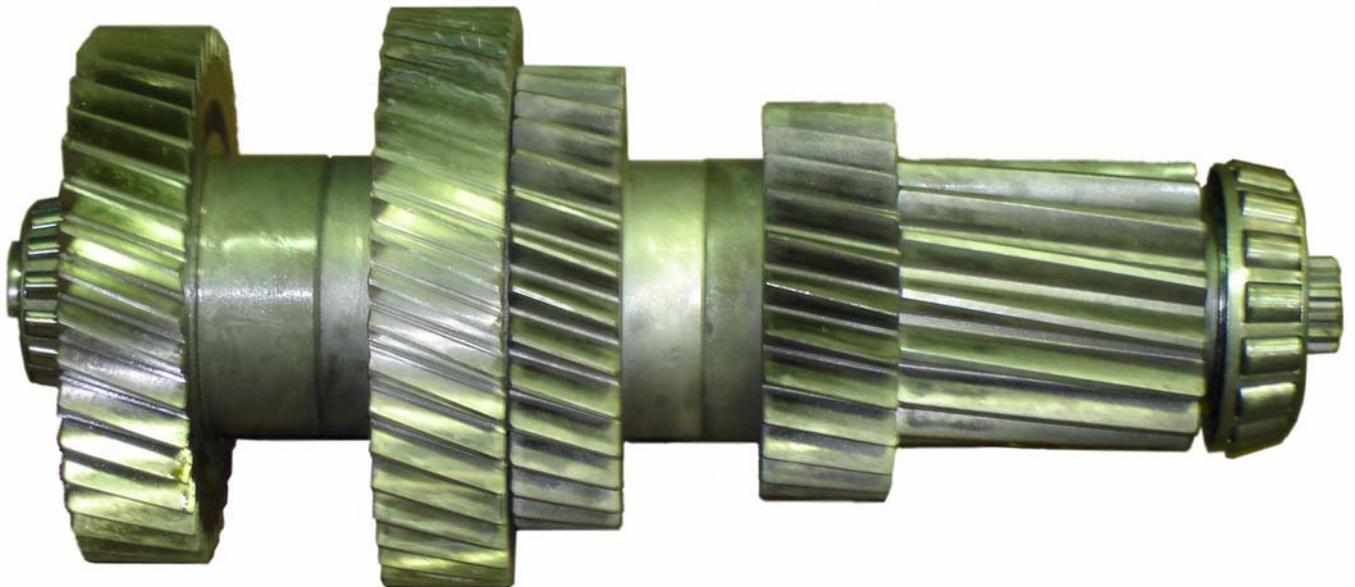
Внешний вид вала первичного в сборе, дет. 239-1701025-10, без наружного кольца подшипника
